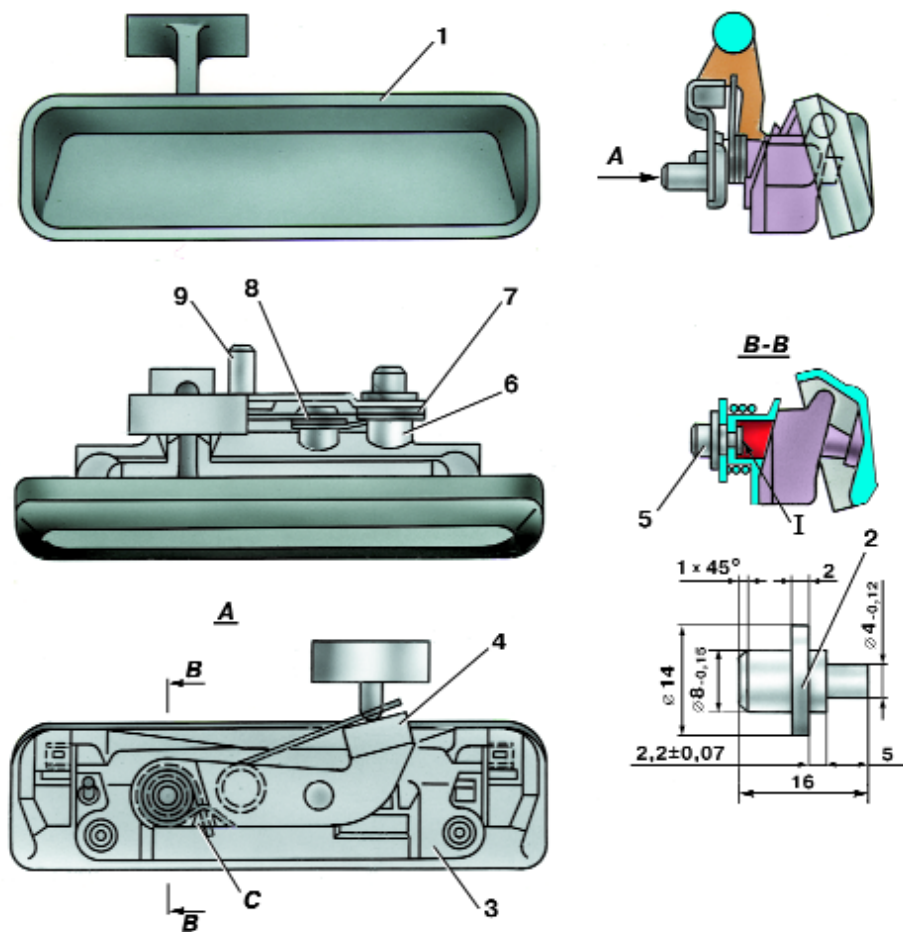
Наружная ручка боковых дверей: 1 – клавиша; 2 – ремонтная ось; 3 – корпус ручки; 4 – рычаг ручки; 5 – ось рычагов; 6 – бобышка; 7 – пружина рычага; 8 – пружина клавиши; 9 – шпилька; I – расклепать, как показано
